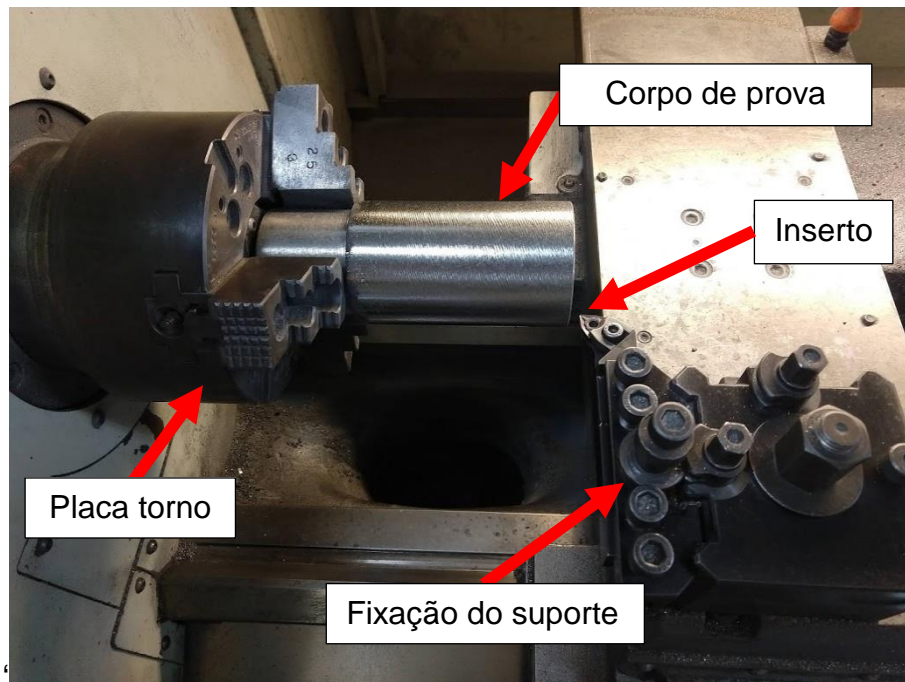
Sistema de fixação do corpo de prova, do suporte da ferramenta e do inserto de corte no torno CNC.
